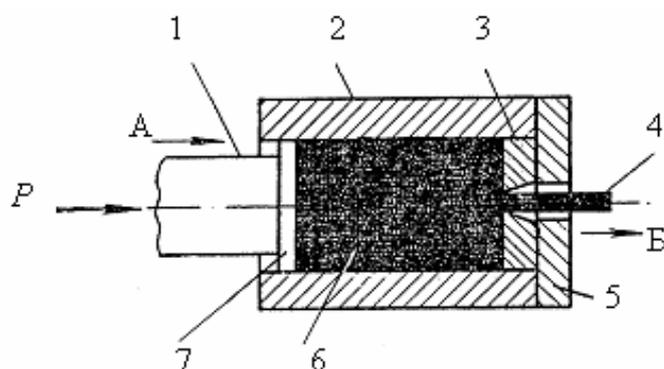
Схема прямого прессования: 1 – пуансон; 2 – контейнер; 3 – матрица; 4 – профиль полученного изделия; 5 – днище контейнера; 6 – заготовка; 7 – пресс-шайба
